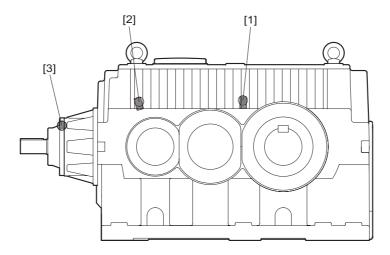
M2P.../M3R... Posiciones de montaje de los adaptadores SPM
